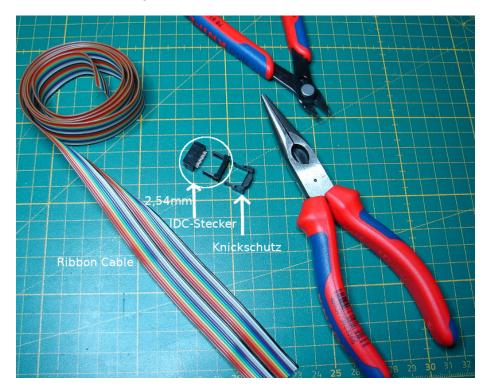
Werkzeug und Ribbon Cable + IDC-Stecker zum selber crimpen
